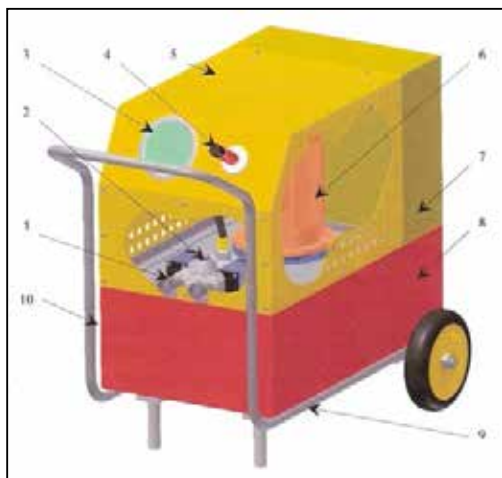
Grup electrohidraulic (Hydramold Iași) pentru acționarea dispozitivelor de pretensionare armături (acționare mecanică a blocajelor)
